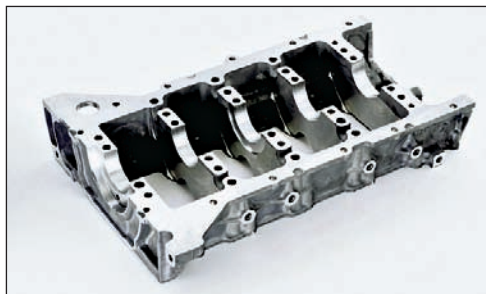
Рама лестничного типа в блоке. Рама лестничного типа заменяют привычные крышки коренных подшипников коленчатого вала в конструкции современных ДВС, придают высокую жесткость блоку цилиндров и продлевают жизнь коленчатому валу
